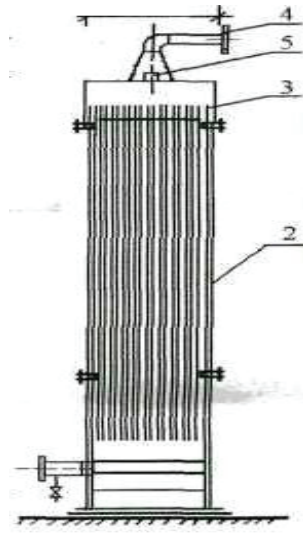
Схема конструкции электрокоагулятора: 1 — питательный патрубок; 2 — съемный корпус; 3 — блок электродов; 4 — отводящий патрубок; 5 — шина для подачи электроэнергии
